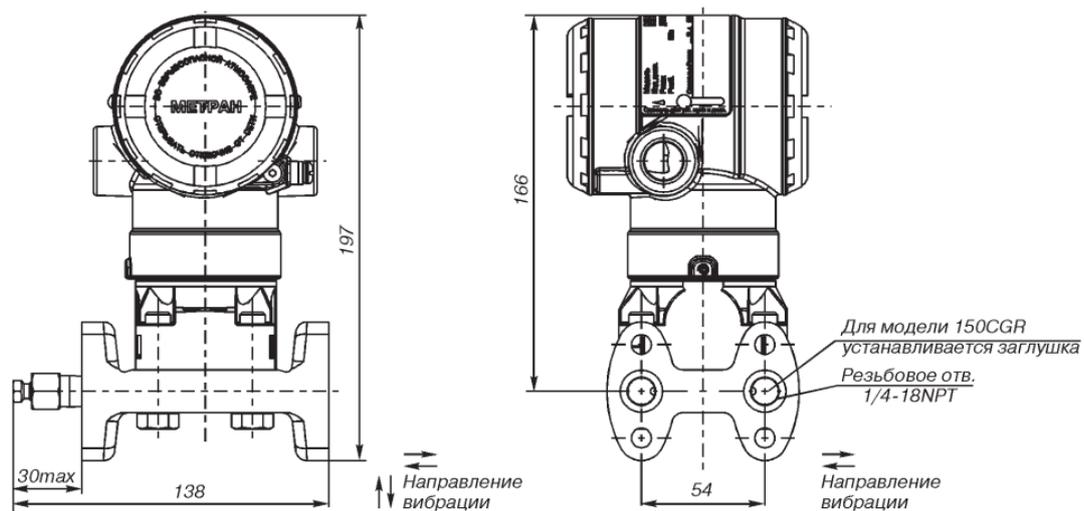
Габаритные и присоединительные размеры Метран-150
